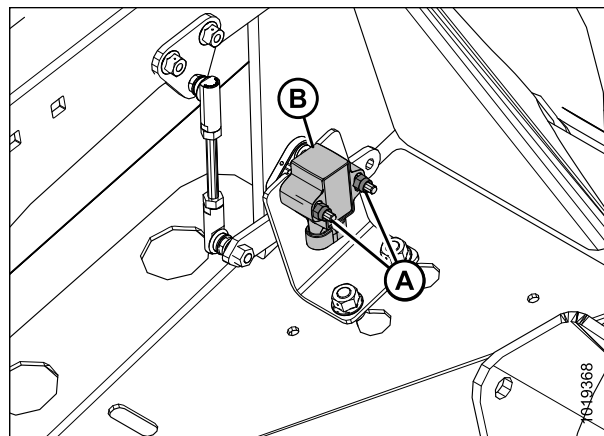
Sensor de altura do molinete – Braço direito do molinete
